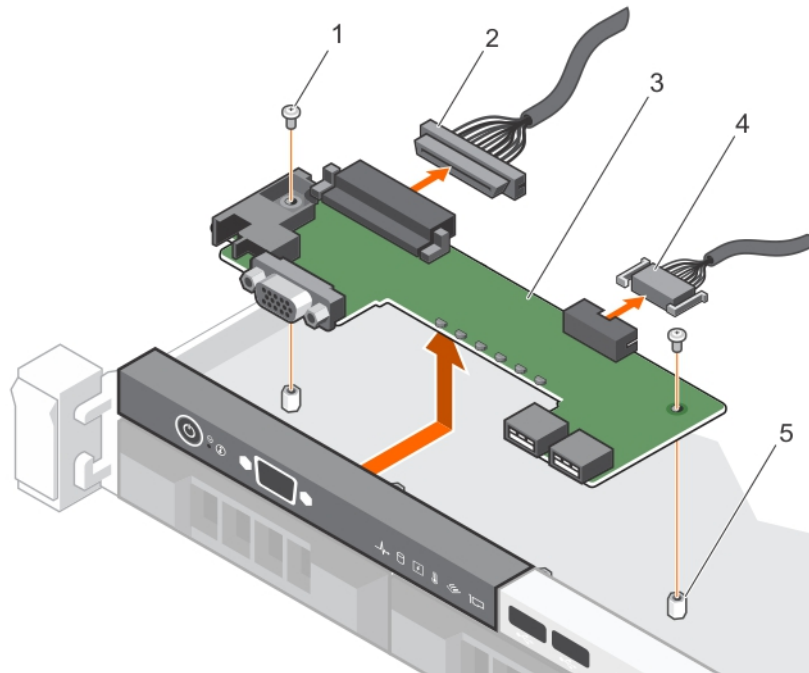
Entfernen der LED-Bedienfeldplatine – Gehäuse für vier verkabelte Festplatten
